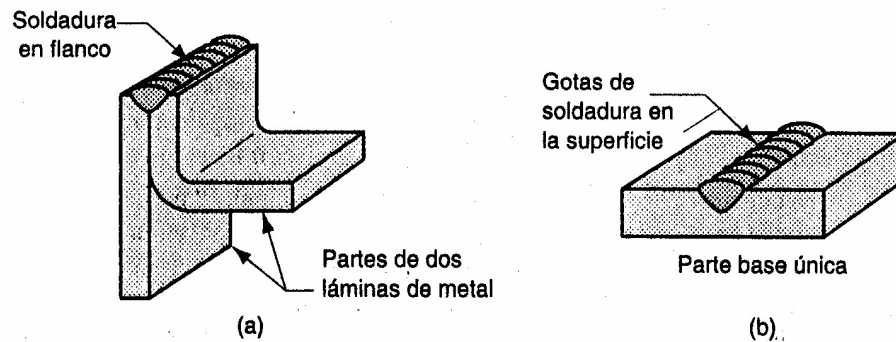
(a) Soldadura en flanco y (b) Soldadura en superficie
